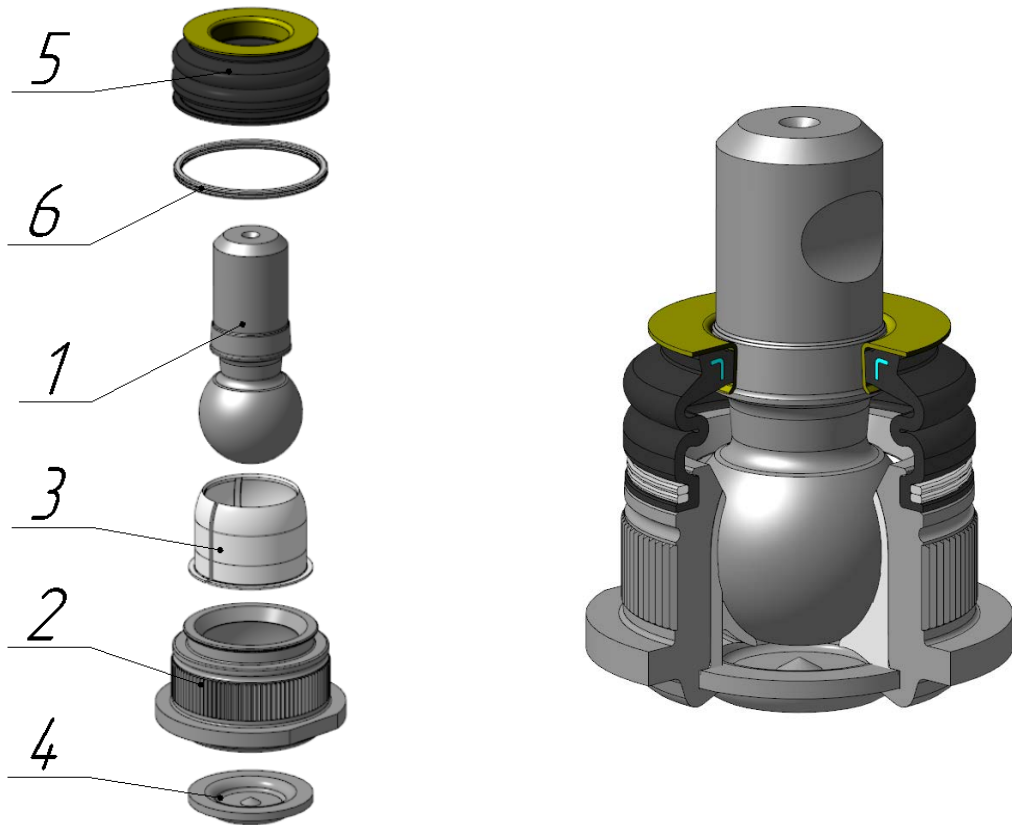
Конструкция шарового шарнира передней подвески автомобиля LADA Largus: 1 – шаровой палец; 2 – корпус; 3 – вкладыш; 4 – обойма; 5 – чехол защитный с отсекателем; 6 – кольцо пружинное
